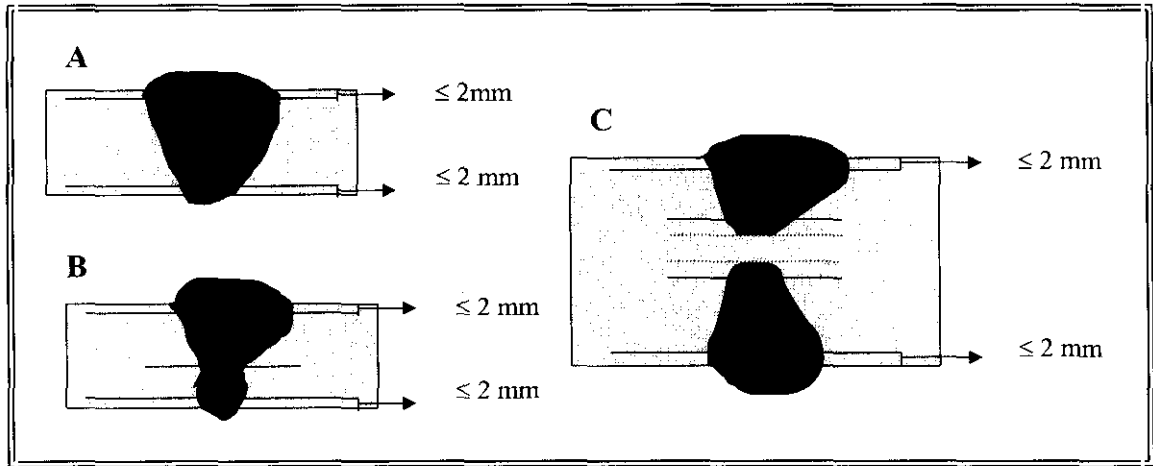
Esquema de medición para obtener perfiles de macrodureza en uniones soldadas
